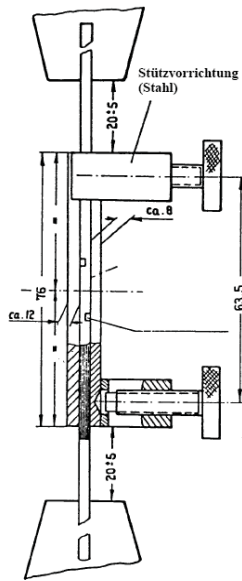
Supporteinheit der Schweißprobenkonfiguration A
